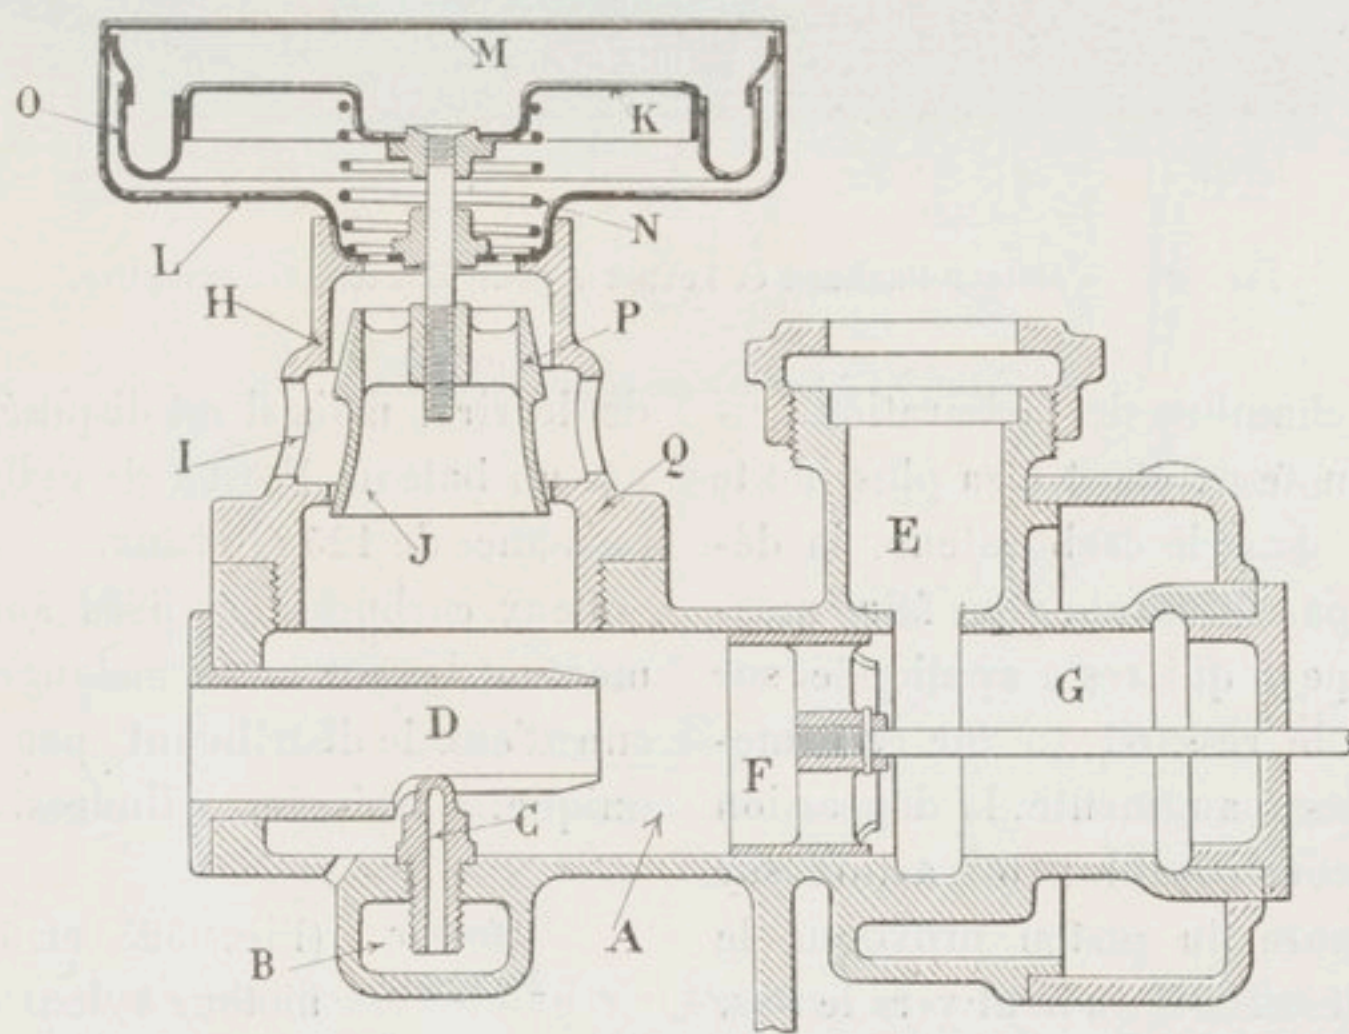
Carburateur à réglage automatique Panhard et Levassor.
